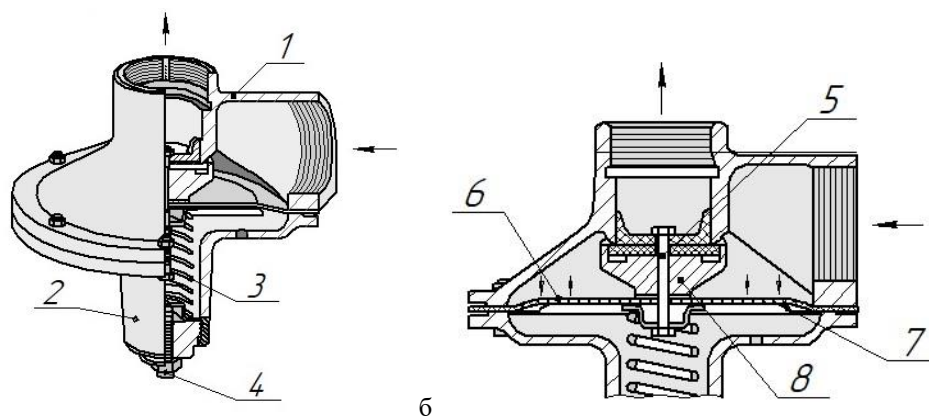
Предохранительно-сбросной клапан (ПСК): а) – внешний вид с  $\frac{1}{4}$  в разрезе; б) разрез; 1 - корпус; 2 - крышка; 3 - пружина; 4 - винт регулировочный; 5 - болт; 6 - мембрана; 7 - тарелка; 8 - клапан
